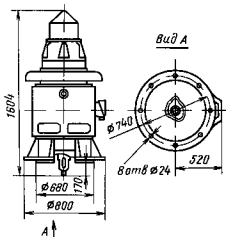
15 Общий вид и основные размеры двигателя серии АВШ, исполнение IM33011 с монолитным валом
